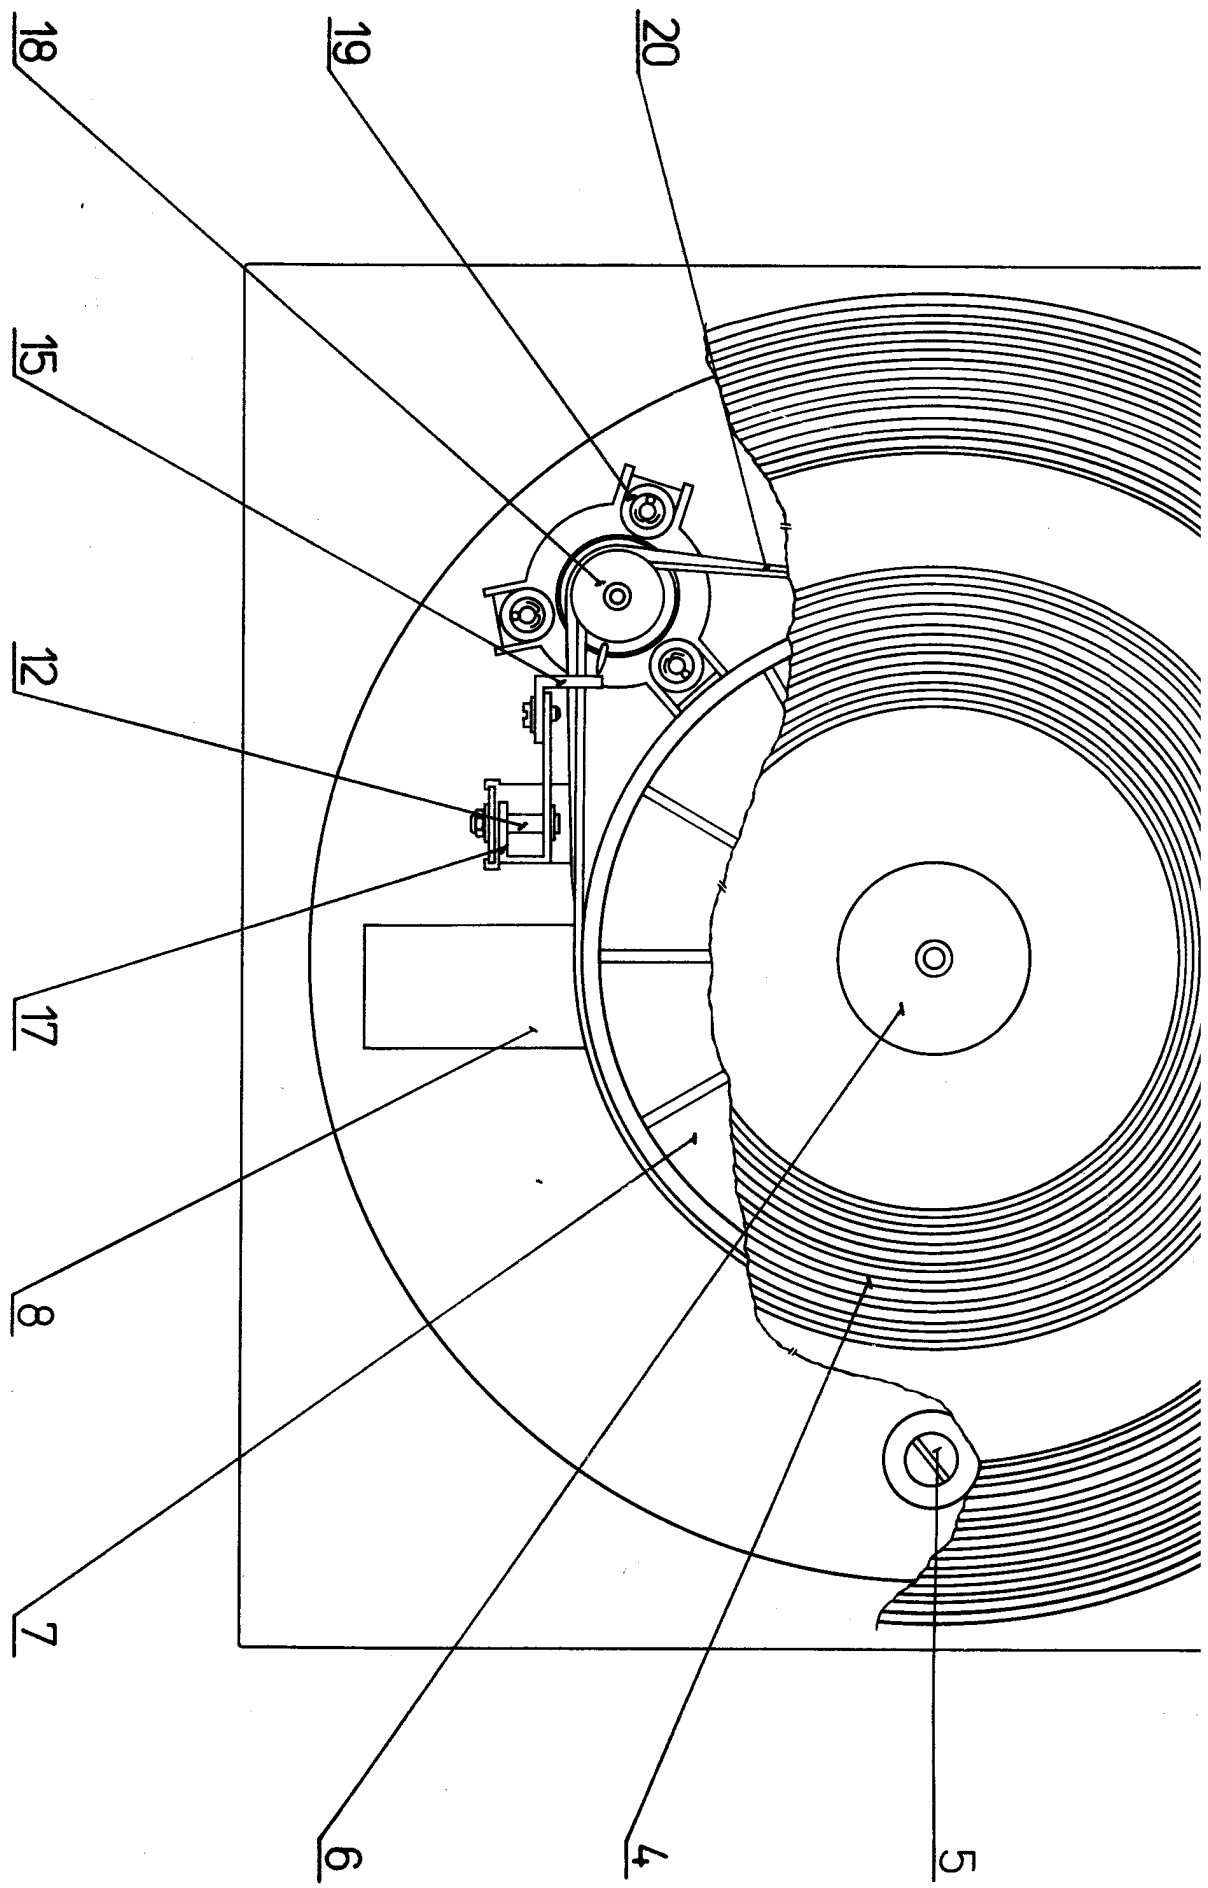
Náhradní a mechanické díly chassis HC 43 - pohled z boku
